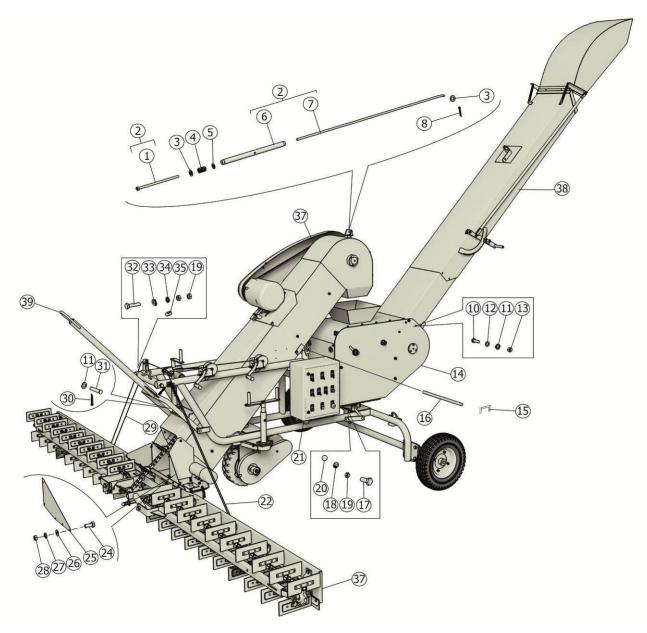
Метатель зерна самопередвижной МЗС-90-20-05МВ/-06МВЧ
